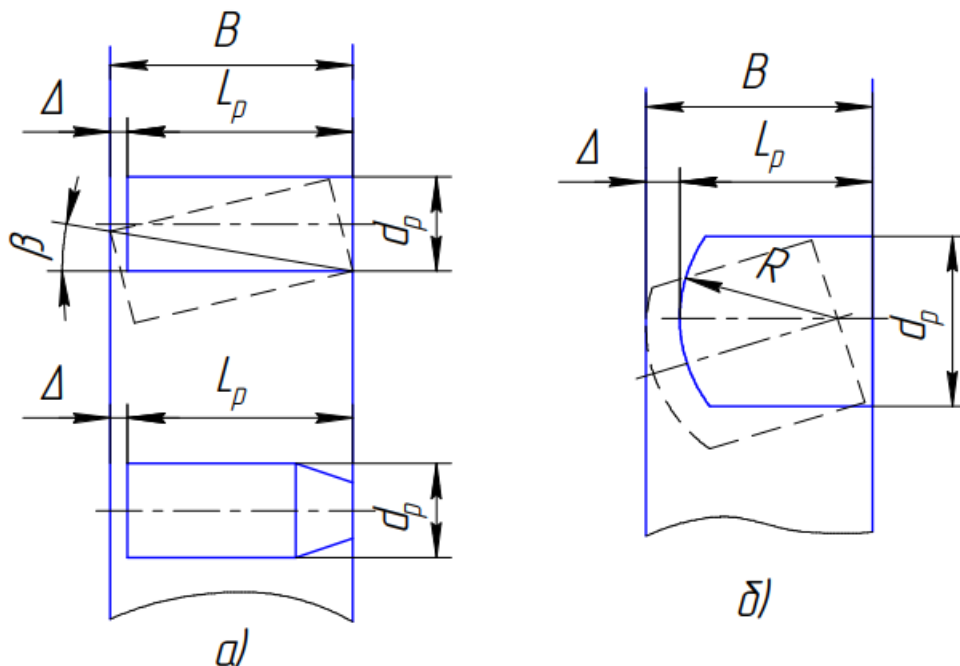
Схема для розрахунку проходження заготовок у лотках
